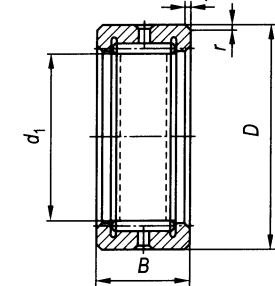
Подшипник роликовый радиальный иглочатый однорядный без внутреннего кольца
